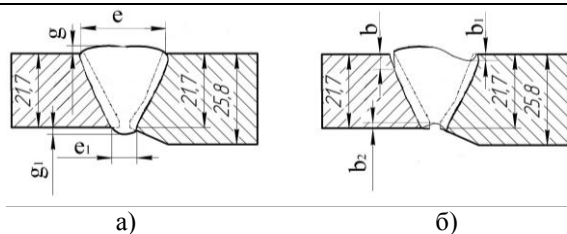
Размеры сварного шва, подлежащие измерительному контролю:
